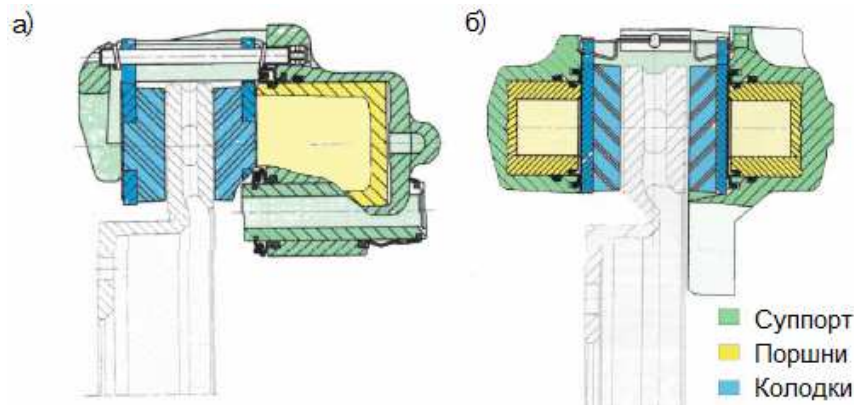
Поперечное сечение скользящего (а) и неподвижного (б) суппорта
